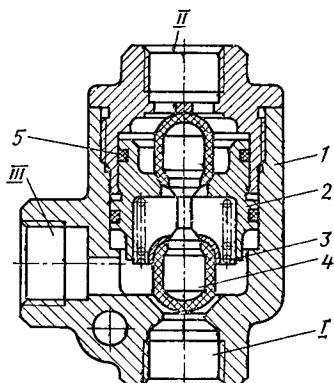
Двухмагистральный перепускной клапан-ограничитель: I—III — выводы; 1 — корпус; 2 — ступенчатый поршень; 3 — пружина; 4 — двойной клапан; 5 — уплотнительное кольцо
